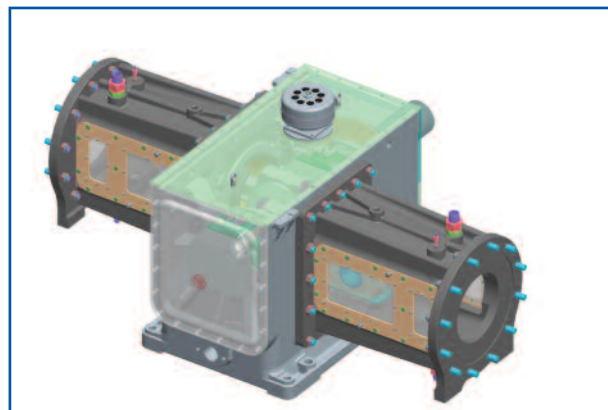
Общий вид унифицированной быстроходной компрессорной базы 2М10А
